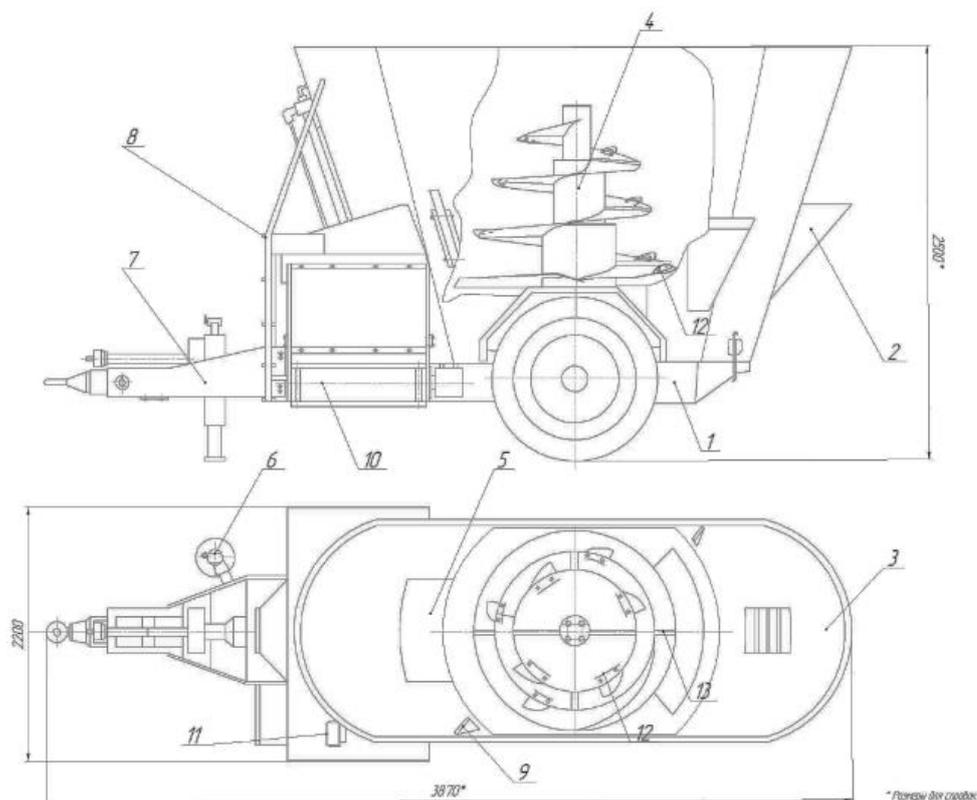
СРК–11В с дополнительными ножами и пластинами
